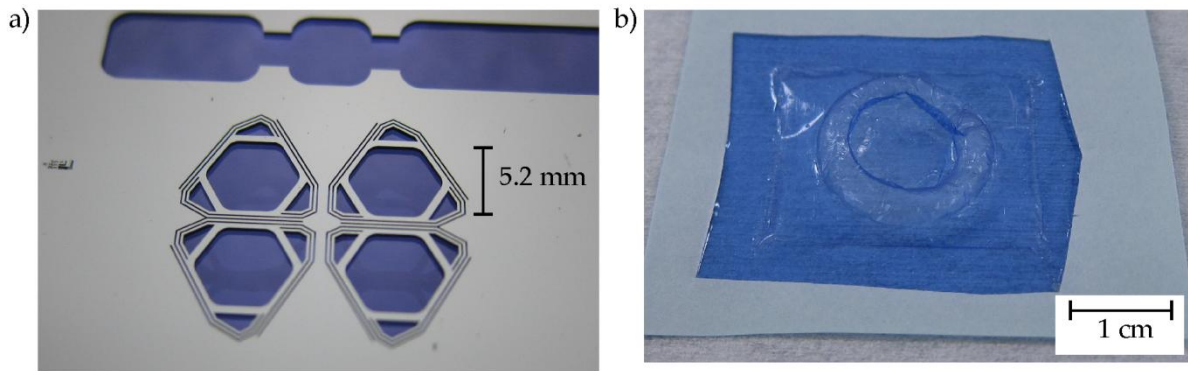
a) Enrésinement de 15 μm de film sec sur des structures entièrement débouchantes de grandes dimensions.
